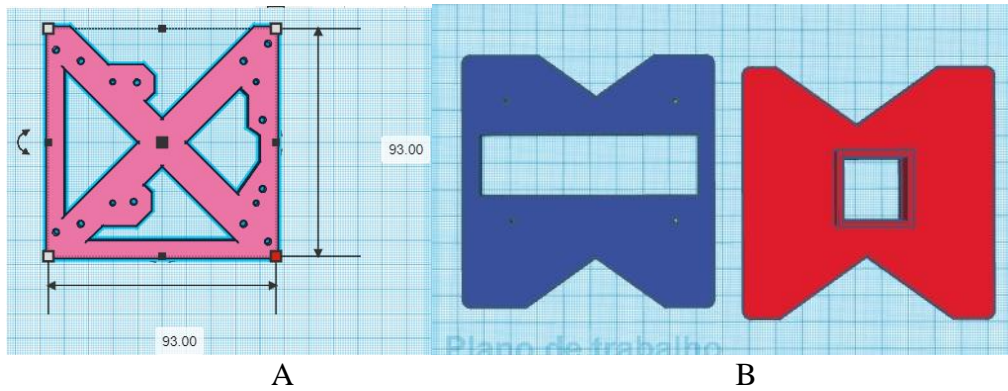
A: Conexão entre a estrutura eletrônica e a estrutura mecânica.
